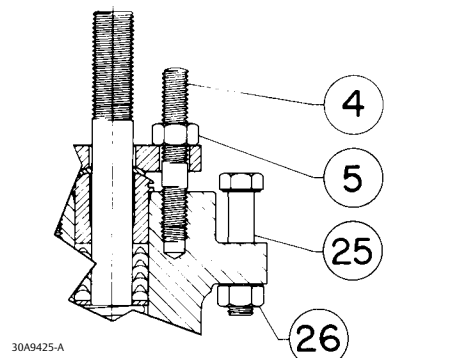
Типовые крышки Fisher с одинарным уплотнением с кольцами V-образного сечения из фторопласта
